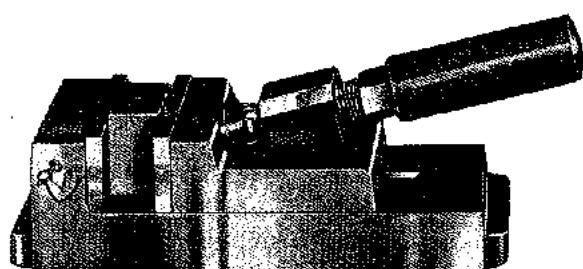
Mordaza de taladradora (Armstrong Bros. Tool Co.)
